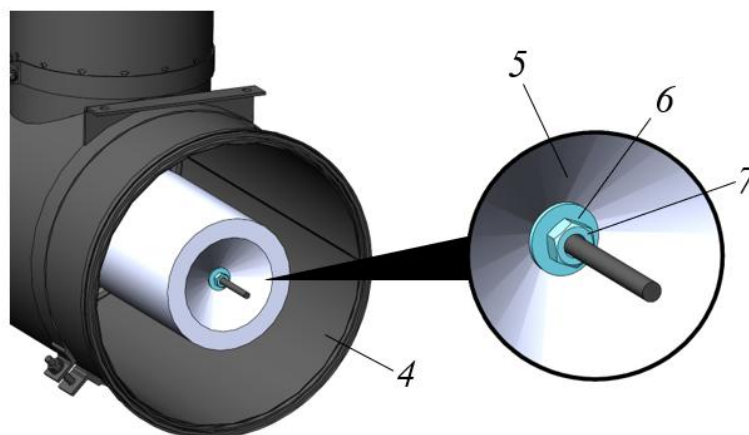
Извлечение из корпуса дополнительного фильтра
